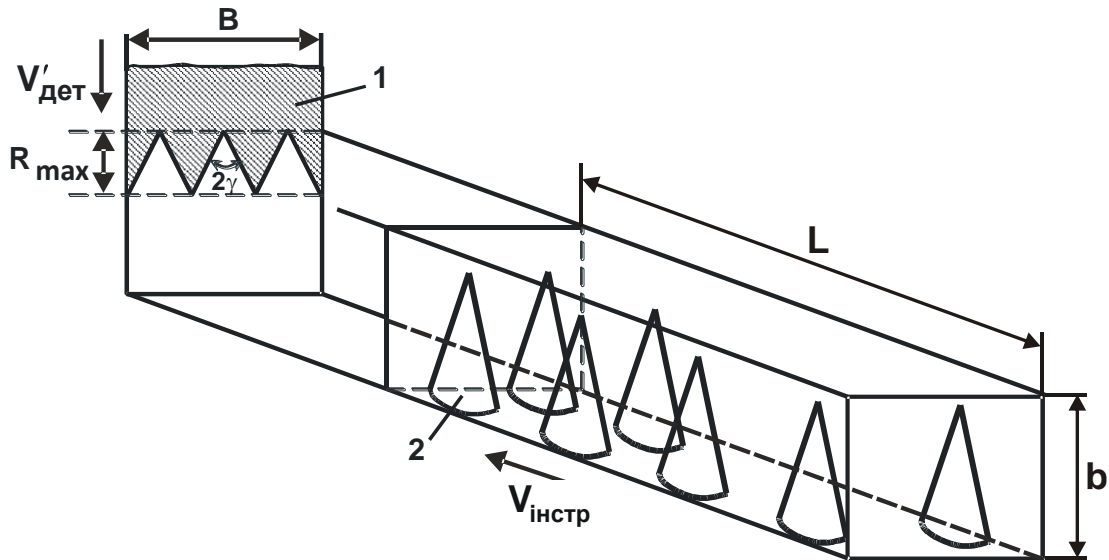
Розрахункова схема формування шорсткості поверхні під час абразивної обробки: 1 – площина оброблюваного зразка; 2 – абразивний інструмент
